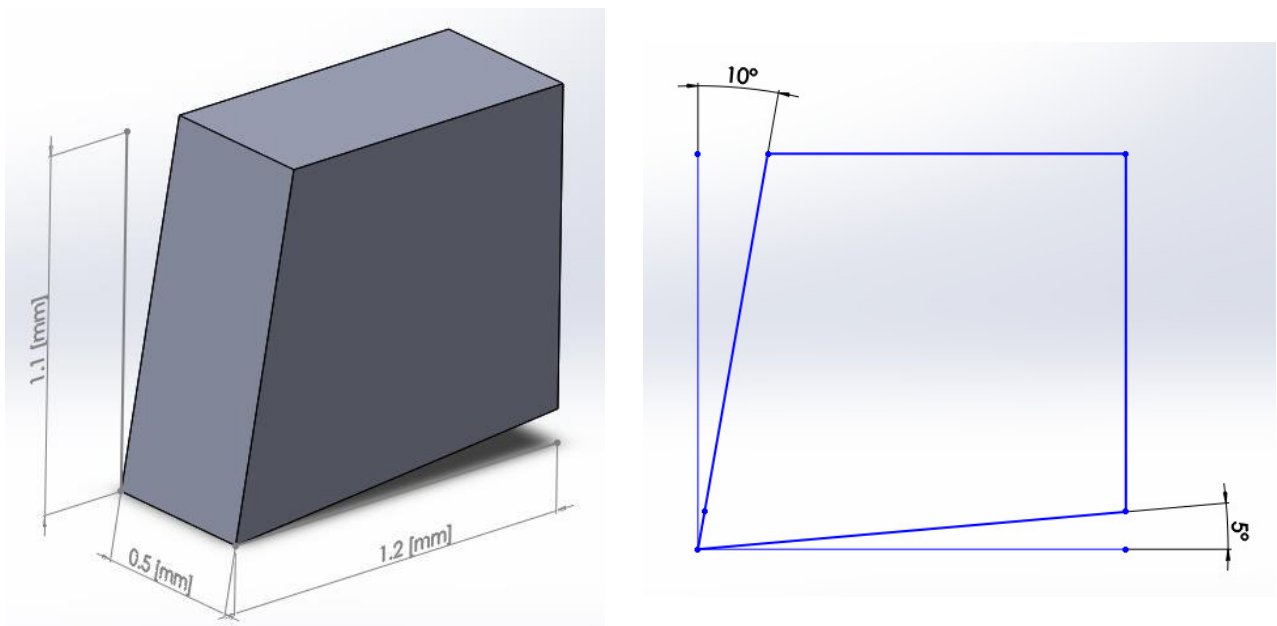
Dimensiones de la herramienta de corte. Ángulos de corte. Dimensiones de corte.
